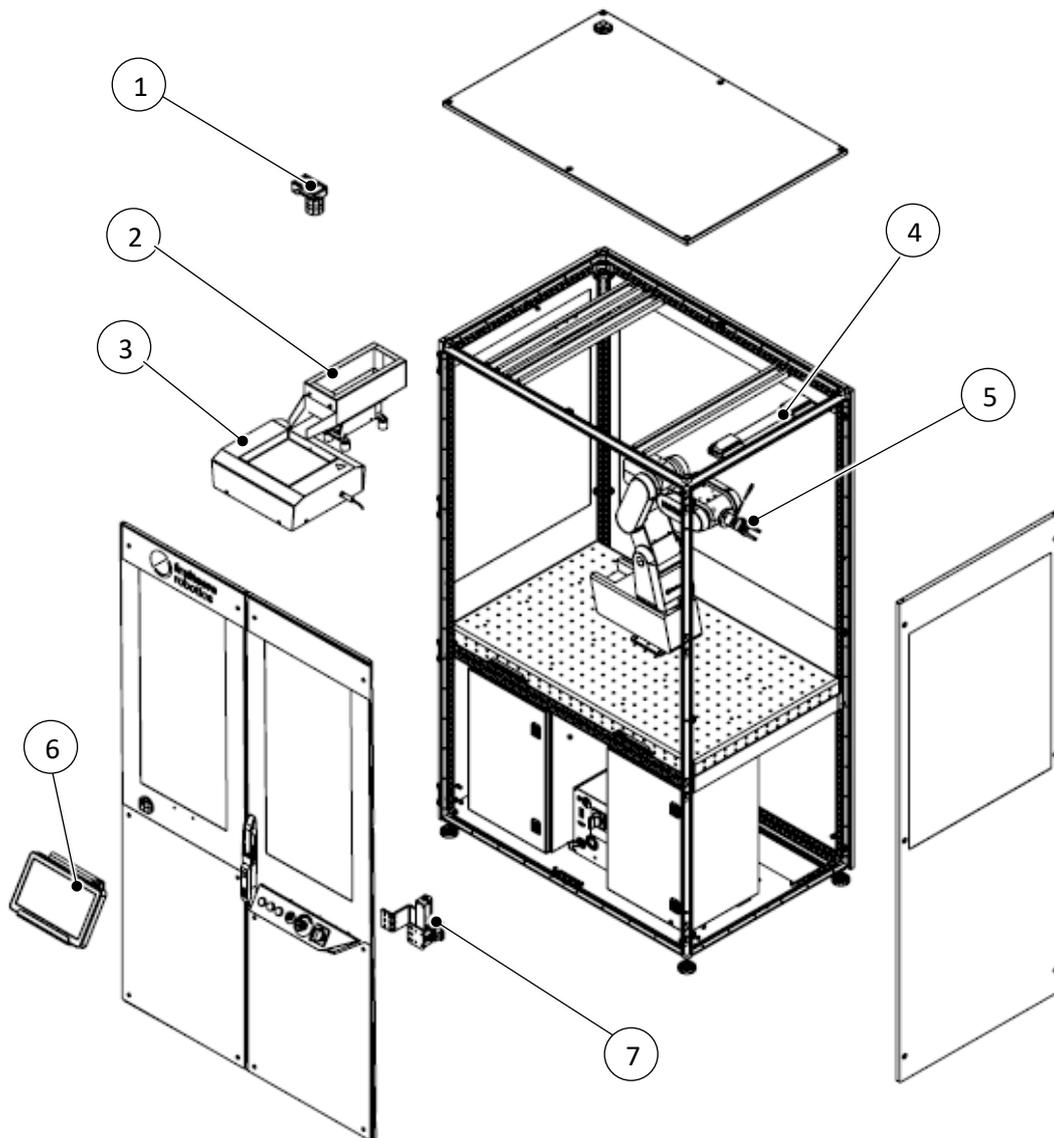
Solution Kit Part Separation - Explosionszeichnung
